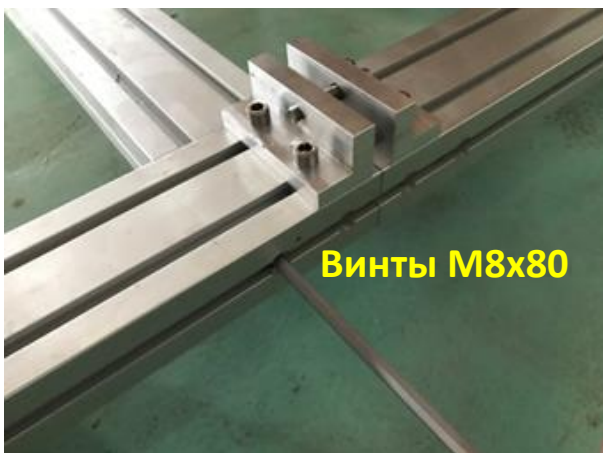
Установка нижней балки 6-ти метрового станка (2500x6000)
